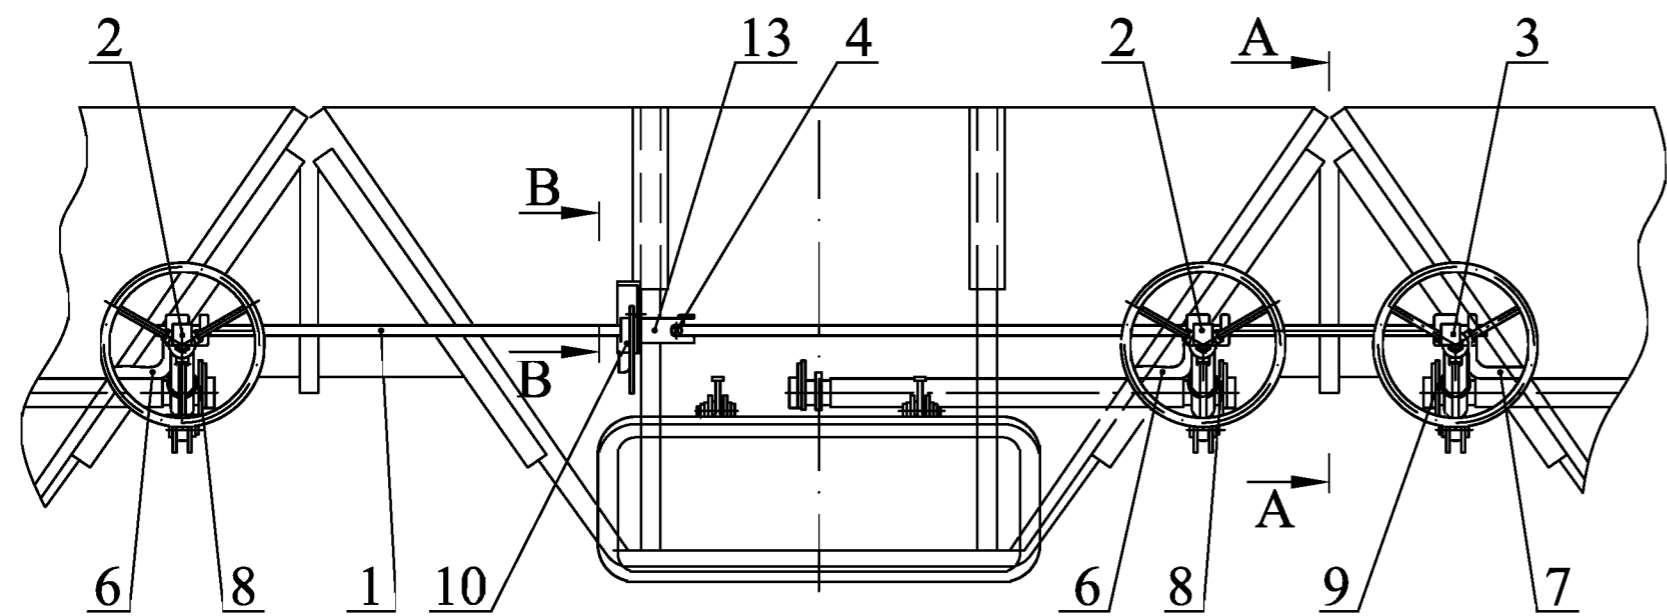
Схема регулировки рычажно-винтового механизма разгрузки и измерения размеров А, В и С
